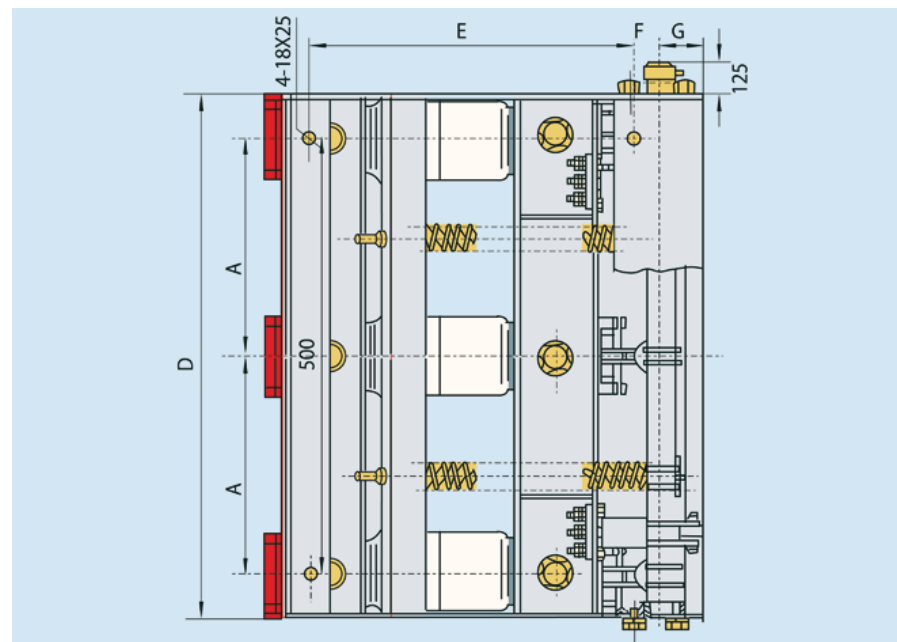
Внешний вид и монтажные размеры выключателя серии ZN28A-12
